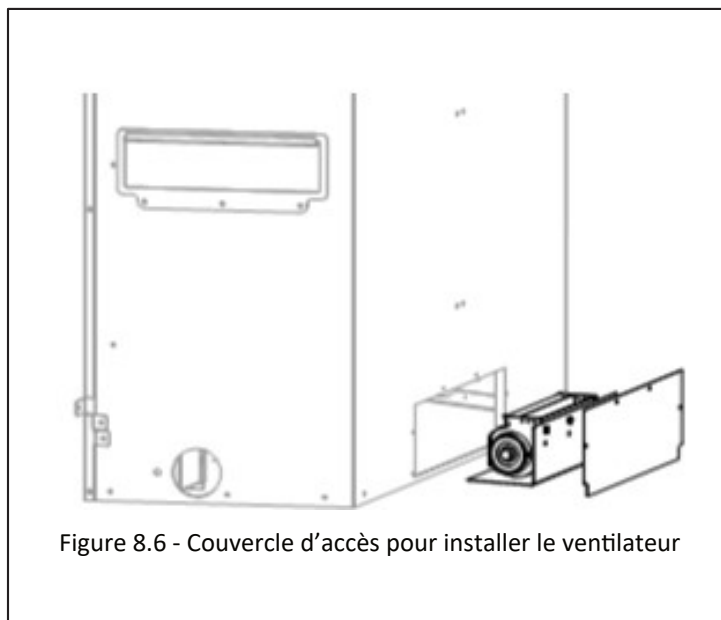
Couvercle d'accès pour installer le ventilateur
